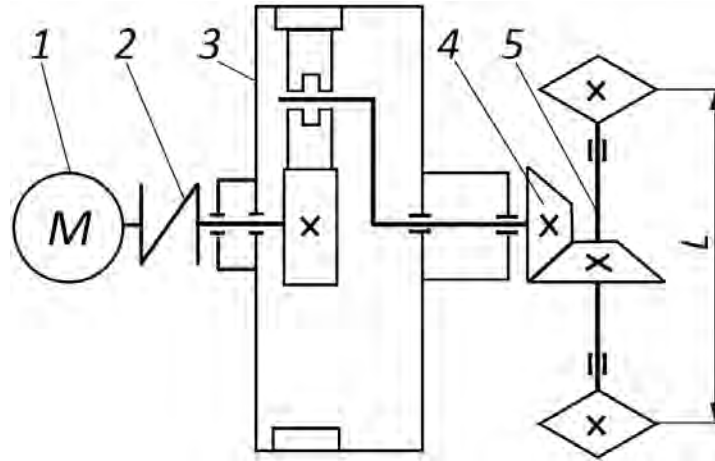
Схема привода цепного конвейера (вид сверху): 1 – асинхронный электродвигатель; 2 – муфта упругая с резиновой звездочкой; 3 – редуктор планетарный зубчатый (по схеме 2К-Н, с тремя сателлитами, с прямозубыми зубчатыми колесами); 4 – открытая коническая прямозубая зубчатая передача; 5 – приводной вал с двумя приводными звездочками
